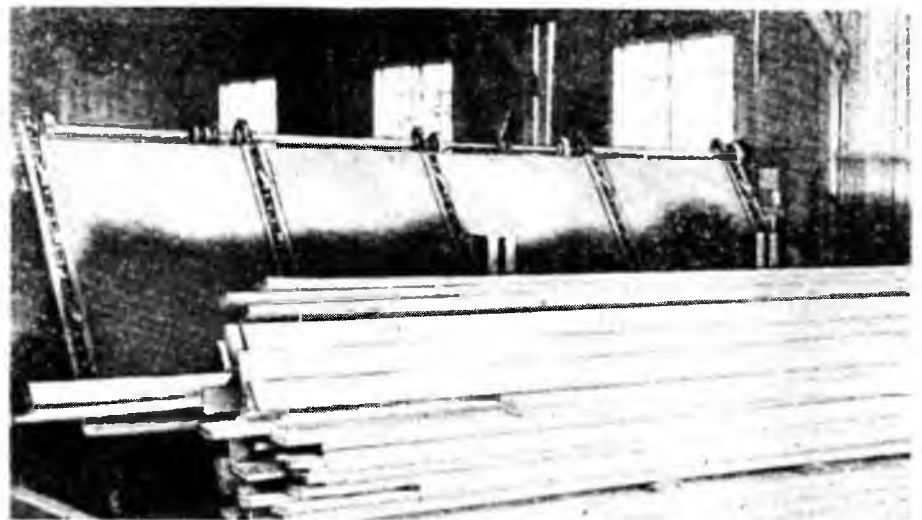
Браковочно-торцовочно-сортировочное устройство на Судской лесобазе
